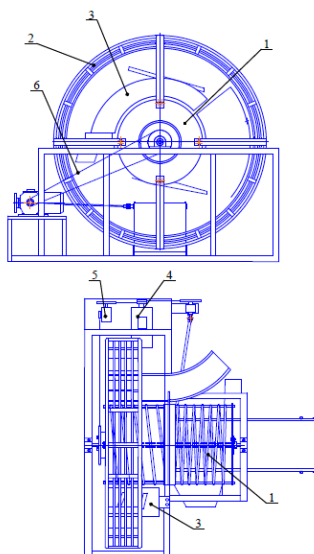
Схема конструкції барабанної сортувальної машини: 1 – сортувальний барабан; 2 – ротор-живильник; 3 – приймальний лоток; 4 – електродвигун; 5 – редуктор; 6 – ланцюгова передача [1].
